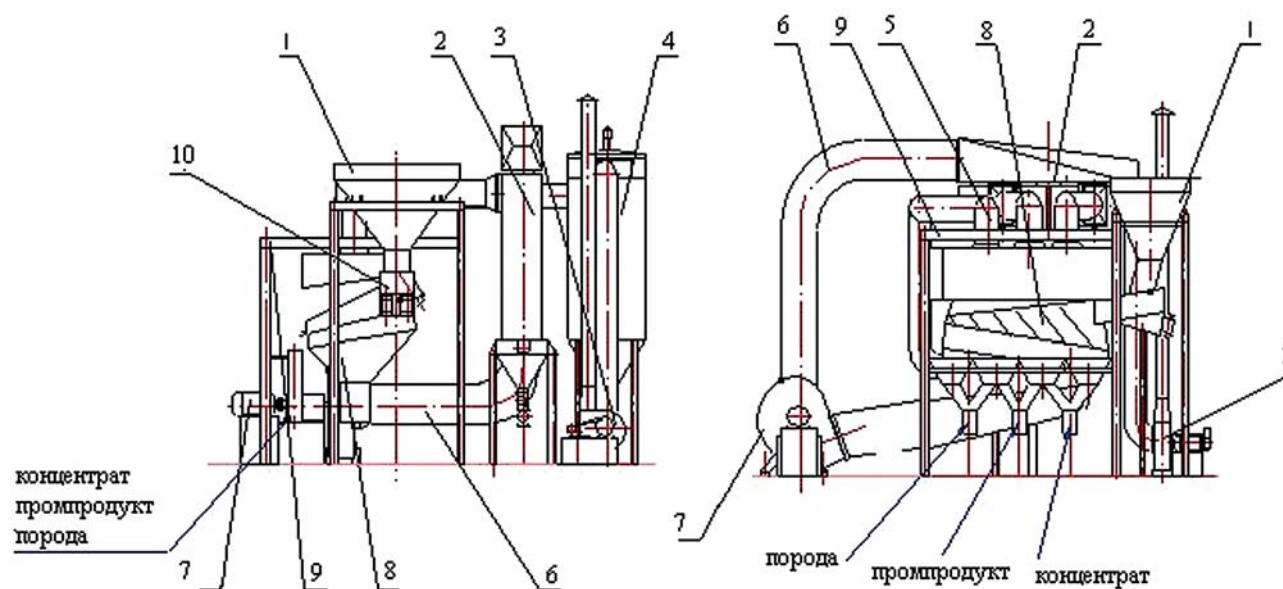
Установка FGX: 1 — промежуточный бункер; 2 — центробежный пылеуловитель; 3 — всасывающий вентилятор; 4 — пылеуловитель; 5 — труба очищенного воздуха; 6 — воздухопровод; 7 — технологический вентилятор; 8 — сепаратор FGX; 9 — рама установки; 10 — вибрационный питатель
